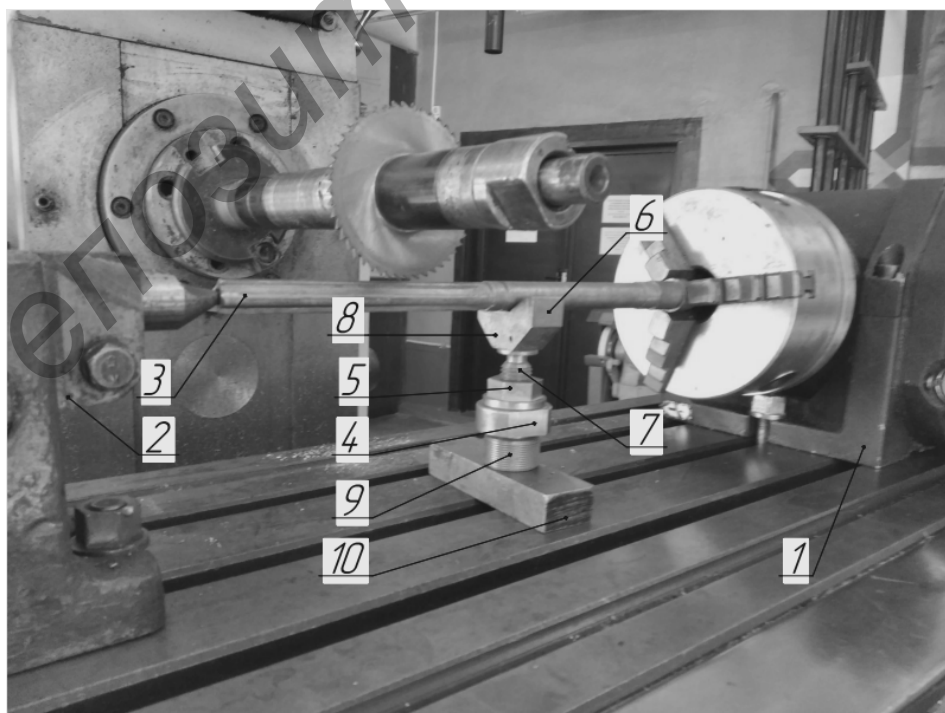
Настройка фрезерного станка на фрезерование шлицев на валу
